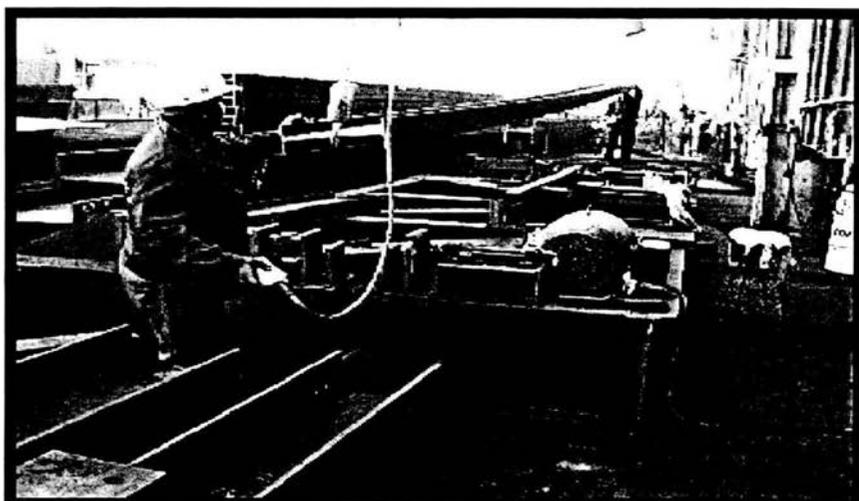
Transporte de perfil barrenado y cortado a la zona de armado para iniciar su fabricación.
